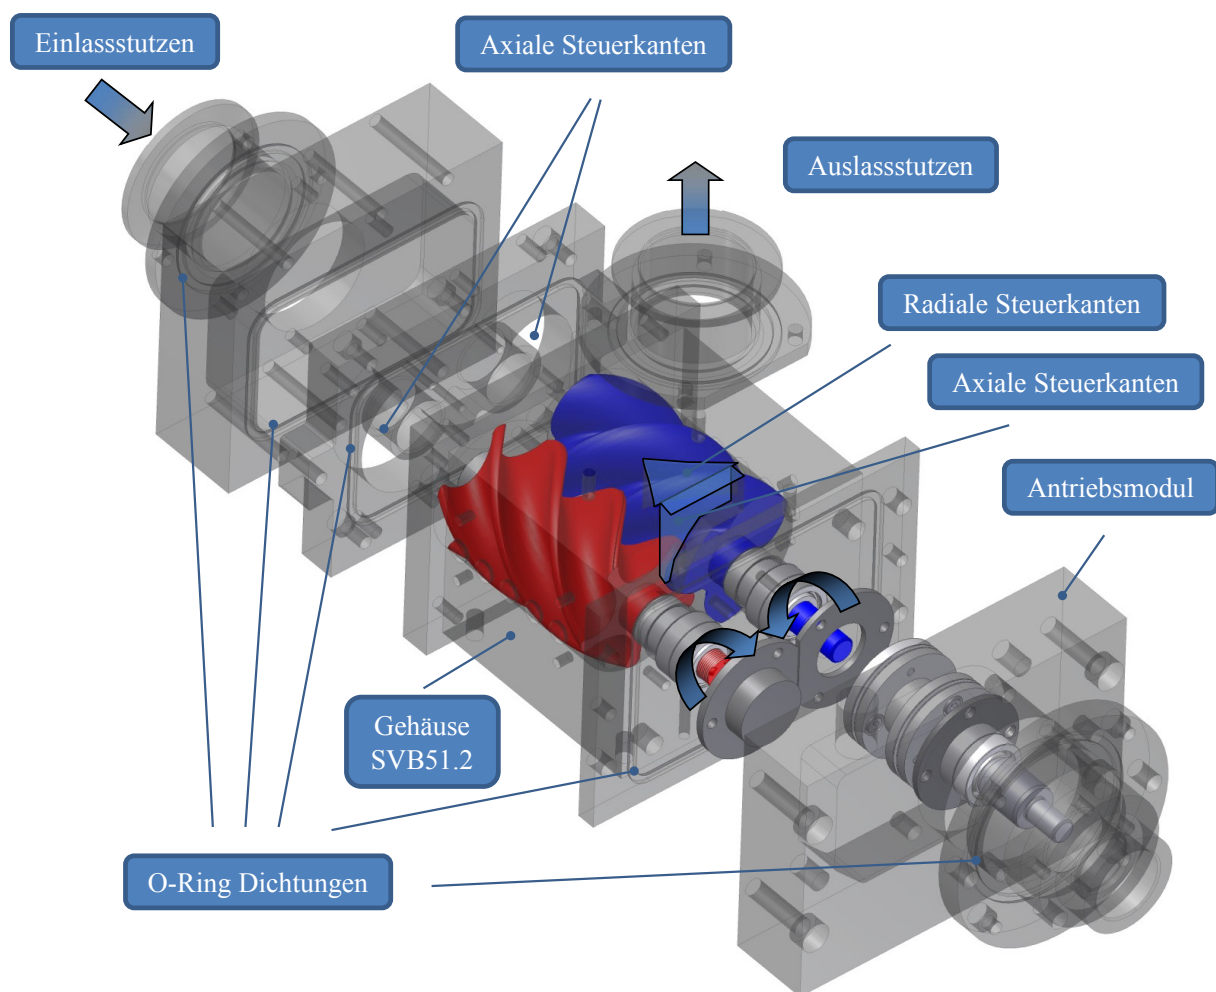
Explosionsdarstellung des Screw Vacuum Blowers SVB 51.2
